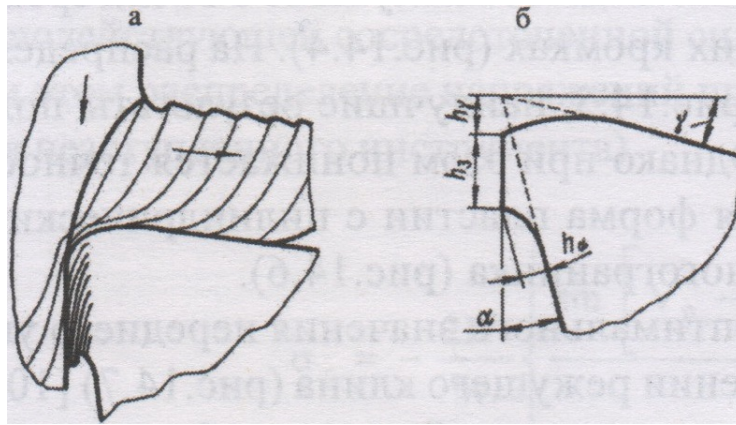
Момент пластичного руйнування ріжучої частини інструменту
